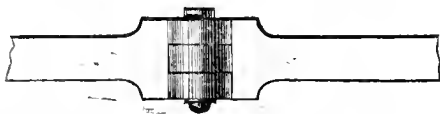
Coupe d'un assemblage à charnières avec boulon à vis.
